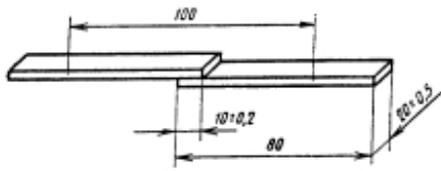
Форма образца для испытания прочности на сдвиг
